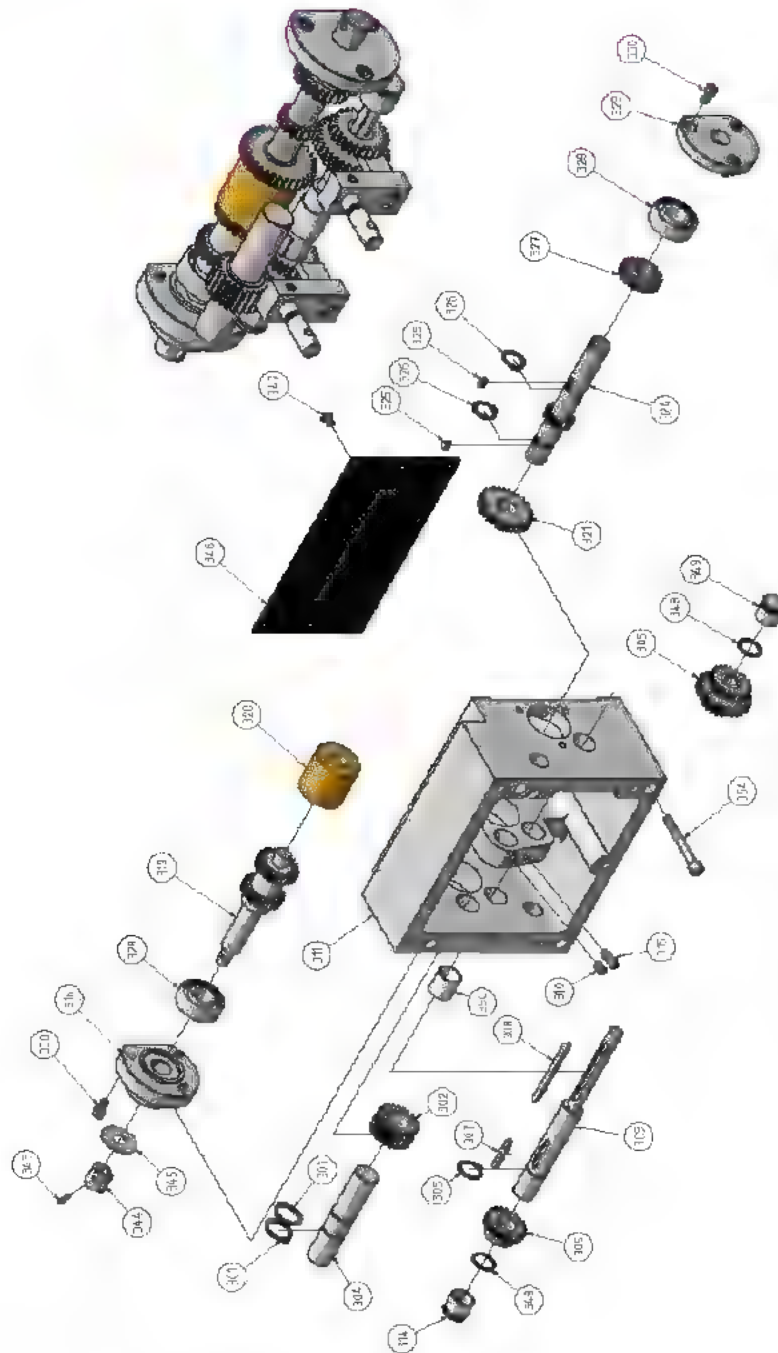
Vorschubgetriebe D280 2 von 2 - Feed gear D280 2 of 2
